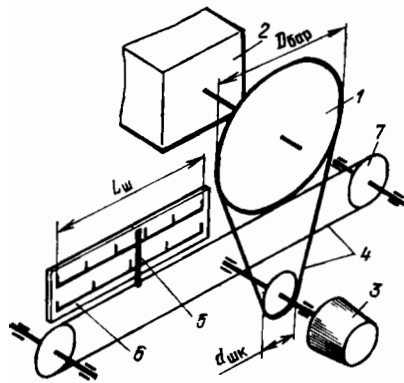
Кинематическая схема настройки с гибкой связью: 1 — барабан; 2 — исполнительный элемент; 3 — ручка настройки; 4 — гибкая связь; 5 — указатель; 6 — шкала; 7 — направляющие стойки
